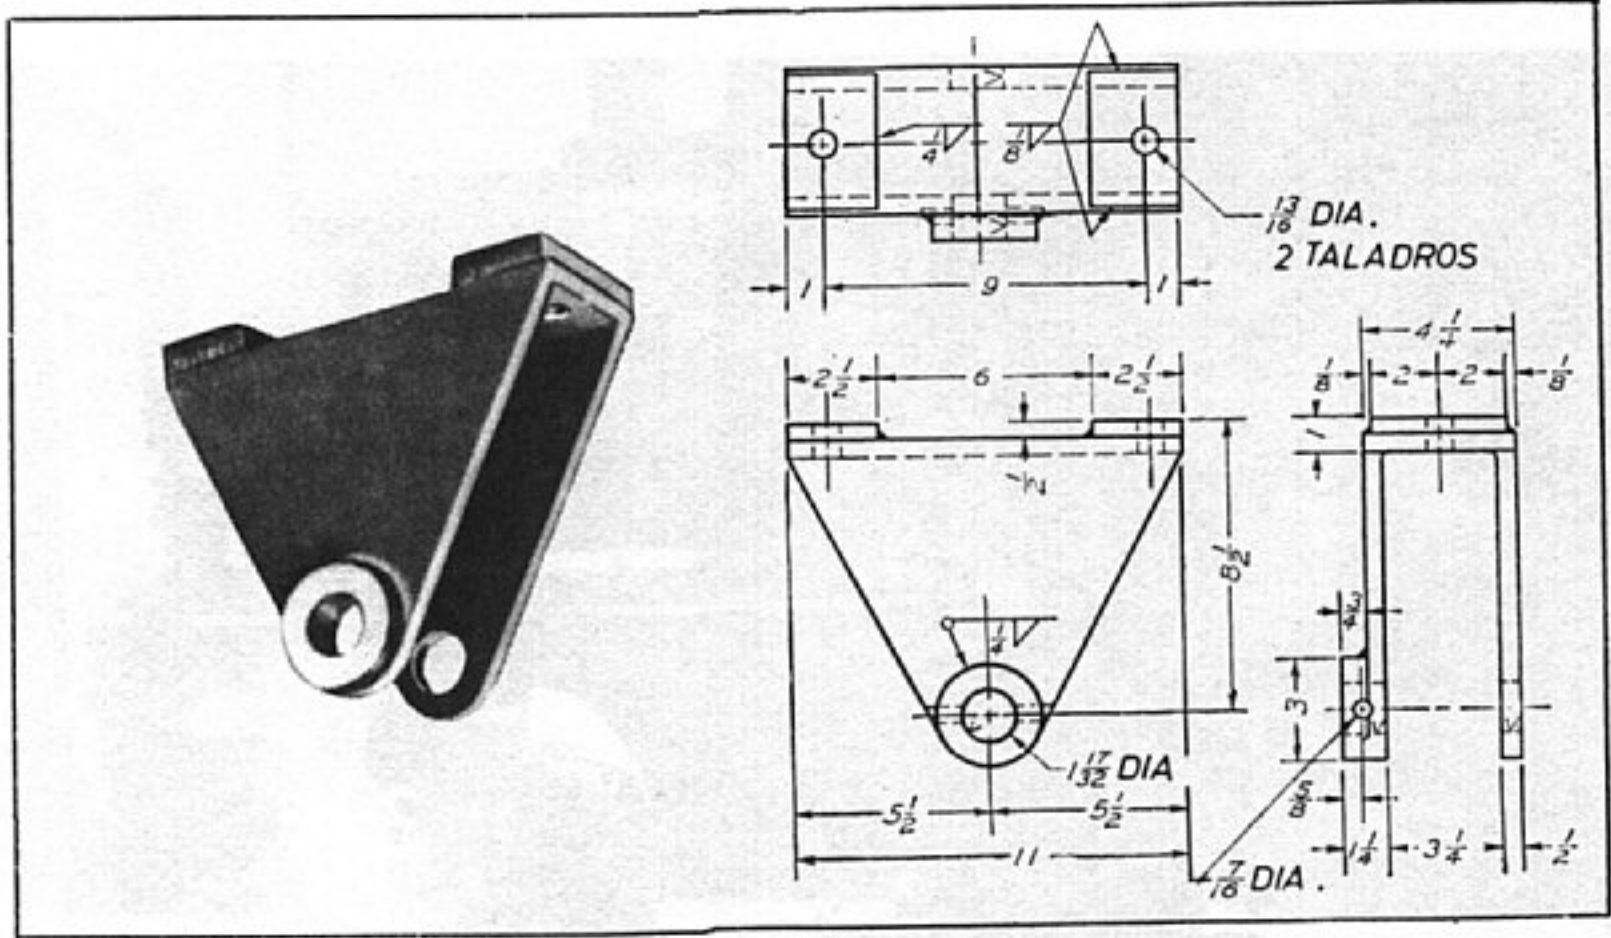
Soporte para polea, soldado. (Wellman Engineering Company and Lincoln Electric Company.) Prob. Q.4.
